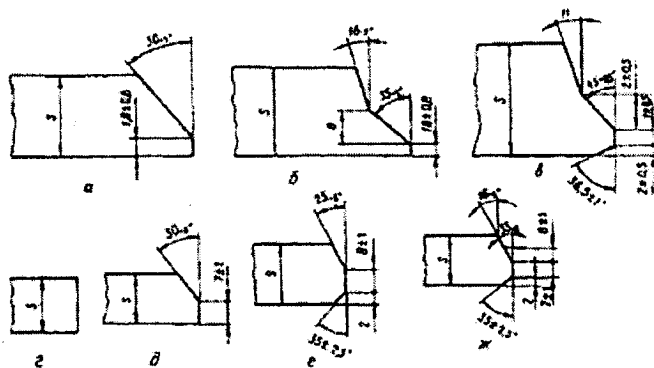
Типи розкриття крайок труб для ручного дугового зварювання (а, б), автоматичного зварювання в середовищі захисних газів (в), автоматичного зварювання під флюсом (г, д, е, ж) и порошковою проволокою (а, б).
